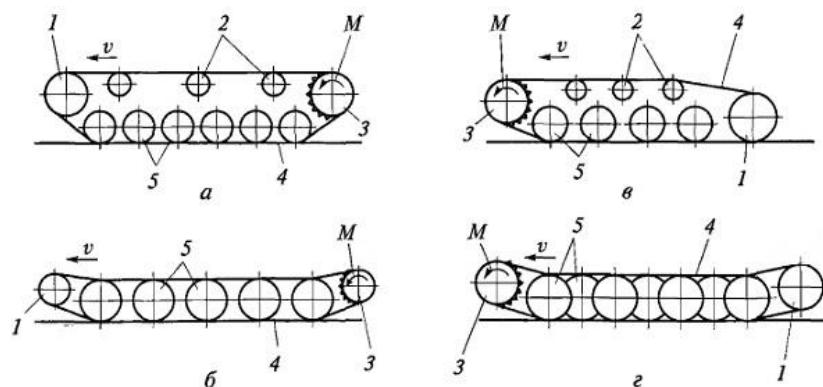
Схемы гусеничных движителей с кормовым (а, б) и носовым (в, г) расположением ведущего колеса:
